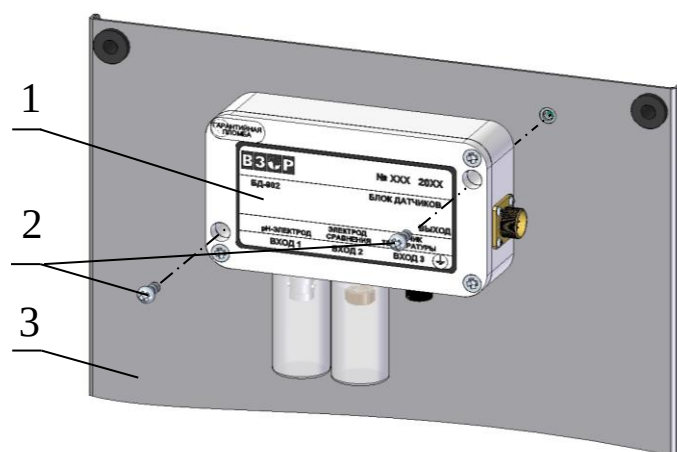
Расположение отверстий для крепления гидрпанели и блока усилителя
